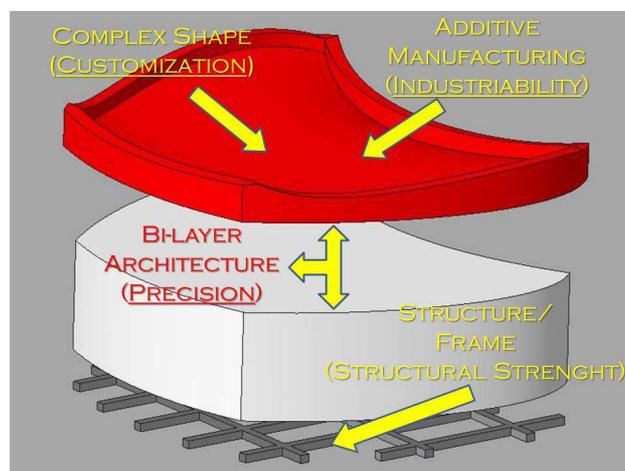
Concetto di Stampo aperto proposto dall’analisi QFD
